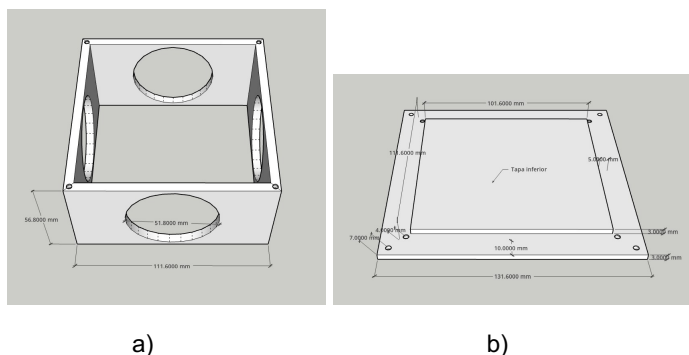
Diseño del MDS. Se muestran las dimensiones.
